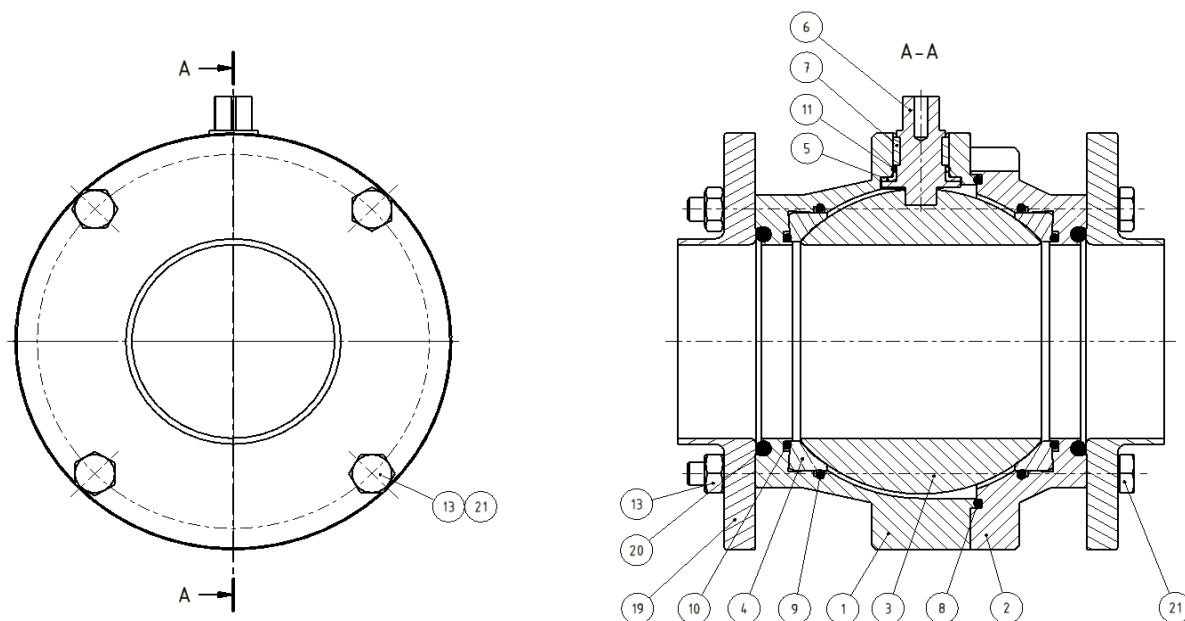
Schnittzeichnung Kugelventil-ZF ohne Betätigung (Zwischenflanschausführung)
